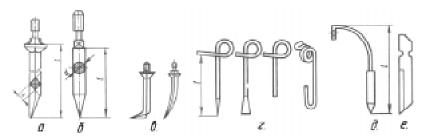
Зубья плоской бороны: a — квадратного сечения; δ — круглого сечения; δ — лапчатый и серповидный; e — пружинные; d — прополочный; e — луговой
